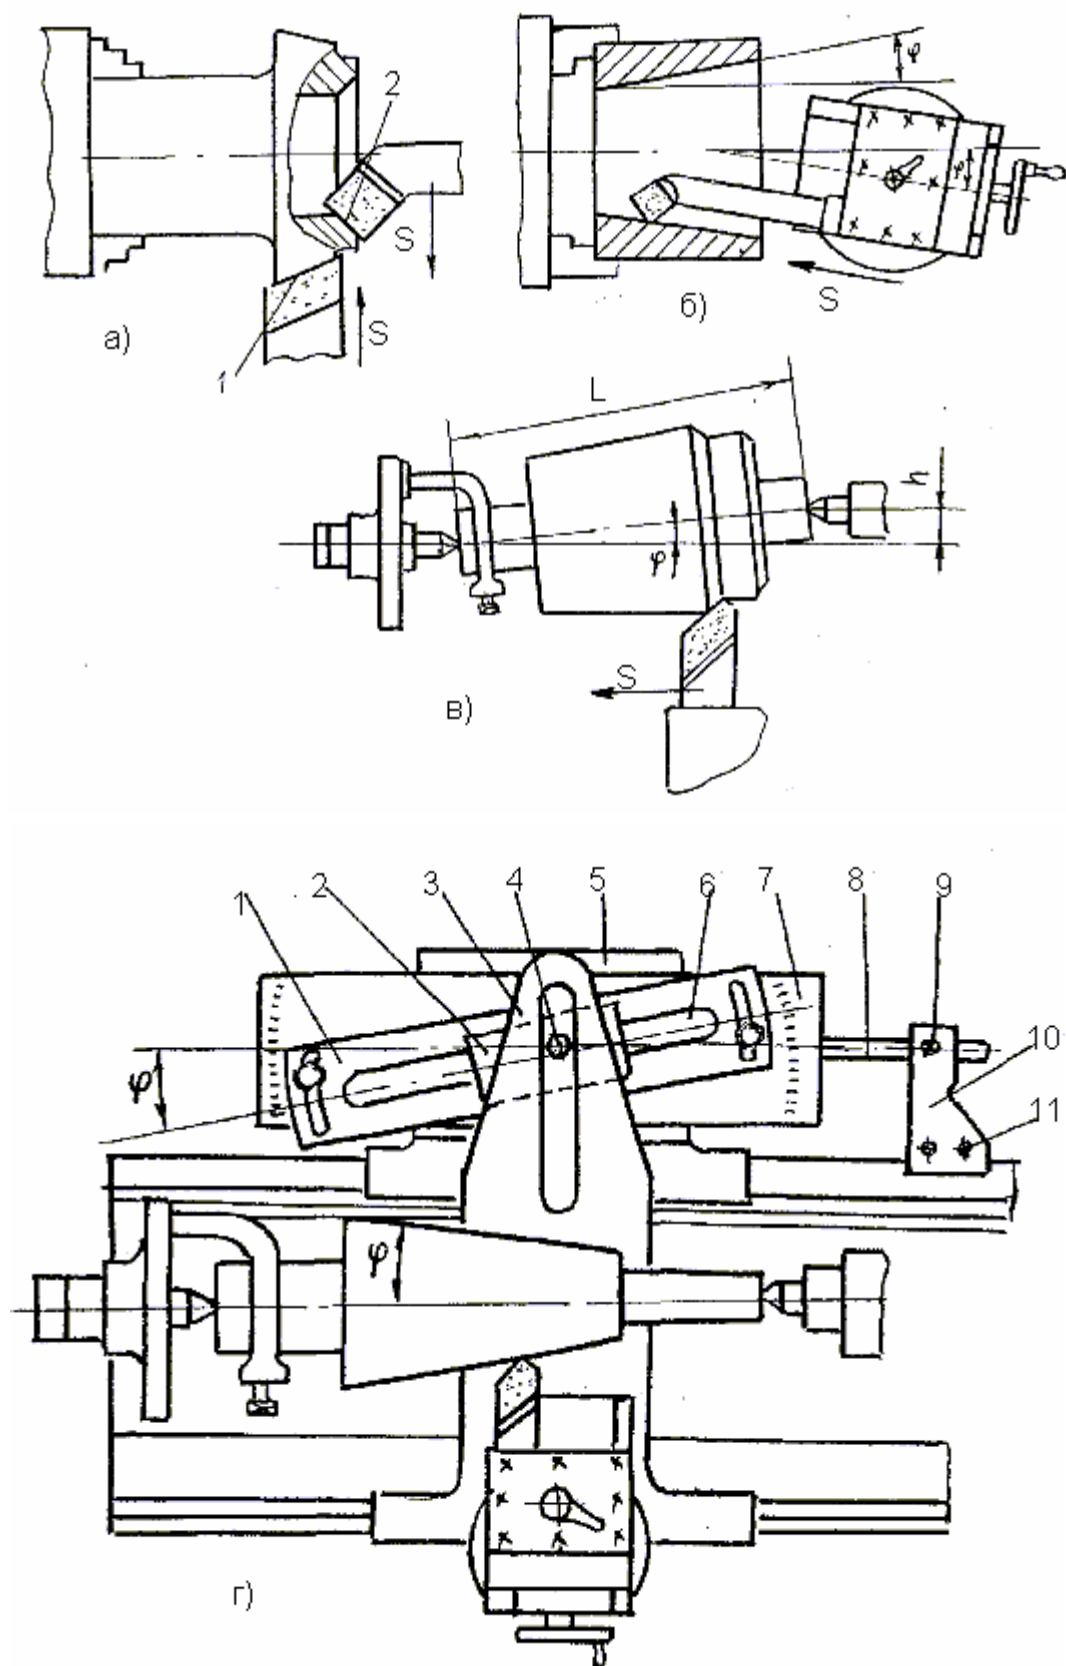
Схеми обробки конічних поверхонь на токарних верстатах
